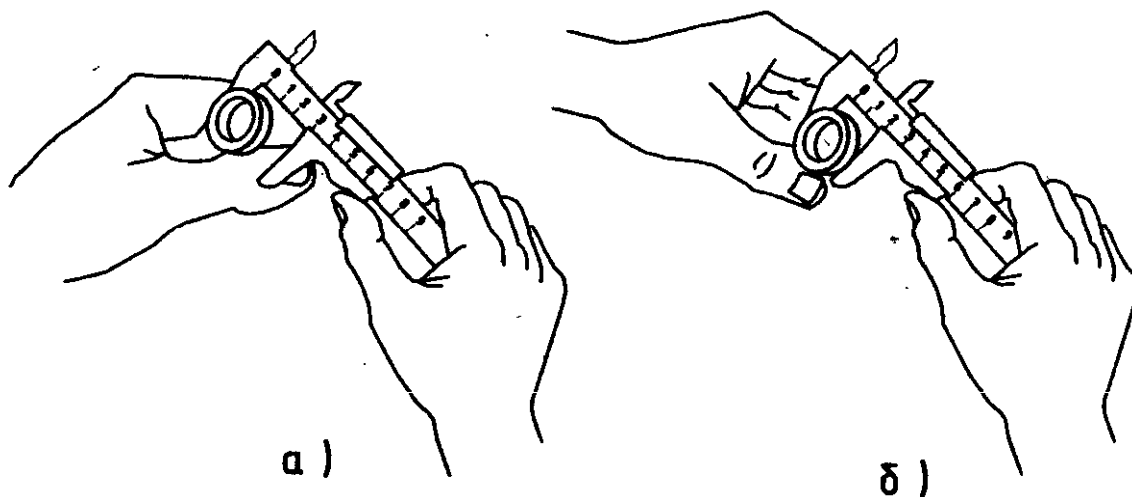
Приемы измерения штангенциркулем диаметров обрабатываемых деталей:
